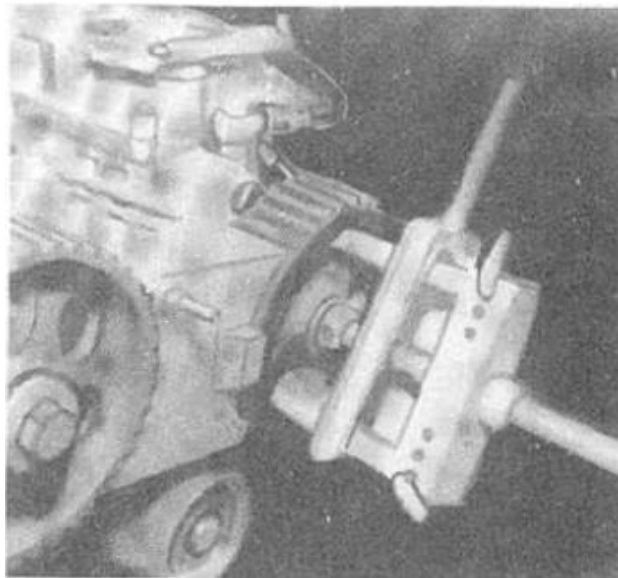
Спресовка зубчатого шкива привода ПНВТ
